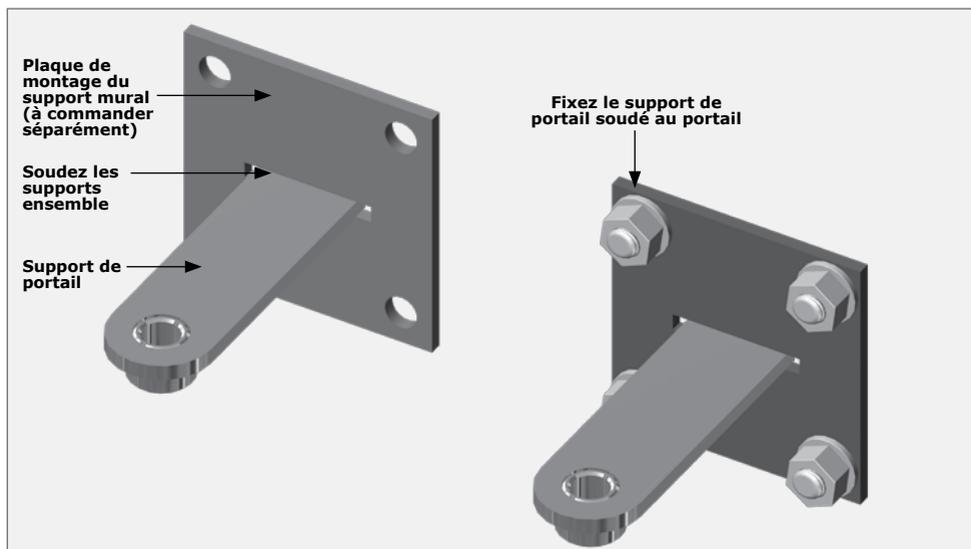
MONTAGE DU SUPPORT DE PORTAIL SUR UN PORTAIL QUI N'EST PAS EN ACIER
